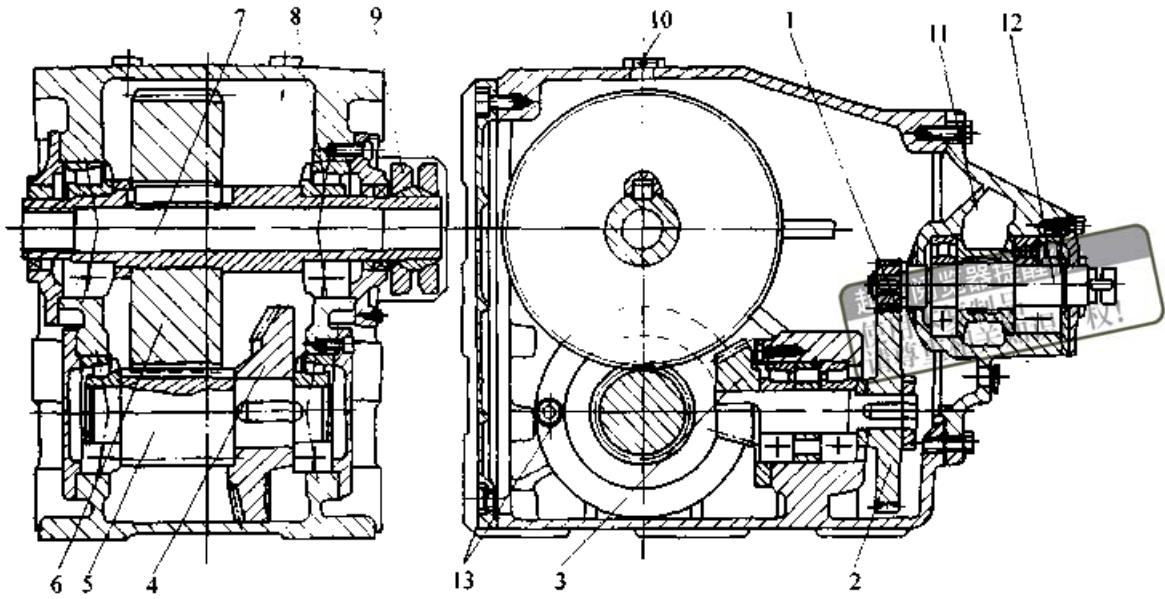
KH160 斜齿轮—锥齿轮减速器
